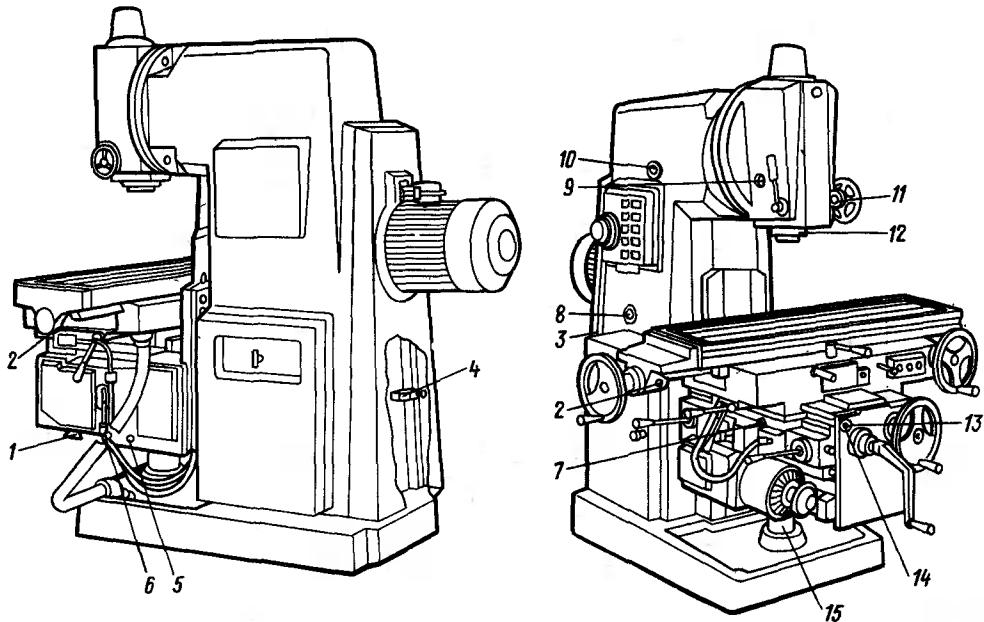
Схема смазки станков 6Р12 и 6Р12Б
